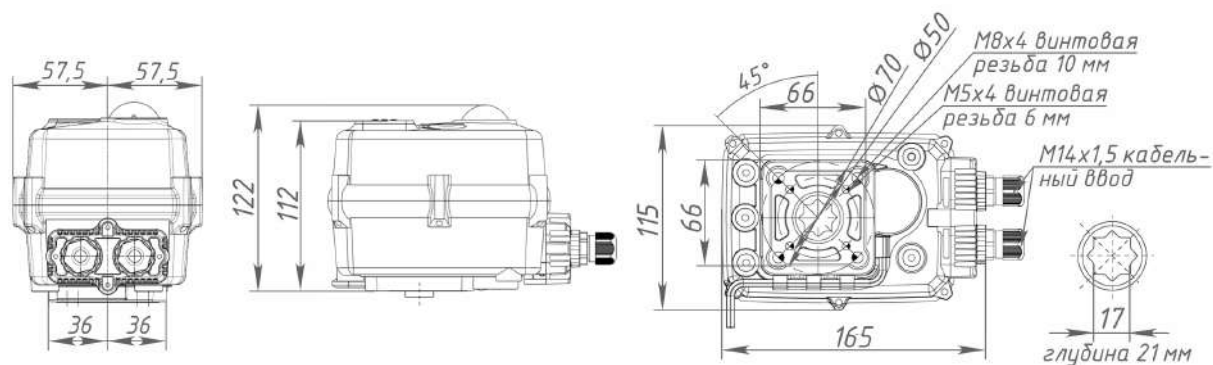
Габаритные размеры электроприводов Motorvalve серий Basic B80 и B110.
